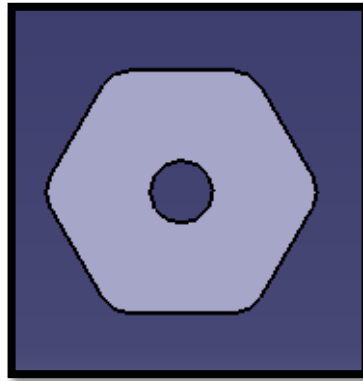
Seat mounting frame 11: Tuerca, hexágono regular de 22.35 mm y agujero de D 10 mm
